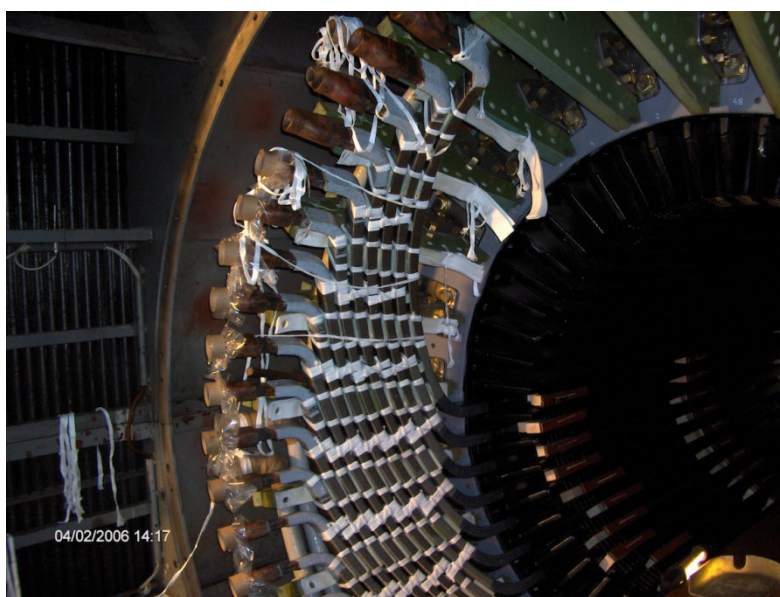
Uložení tyčí v drážce (převzato z [5])
